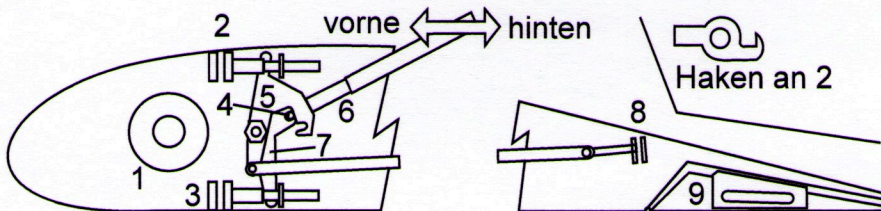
Holmanschluss rechter Flügel vom Rumpf her gesehen, entriegelt
